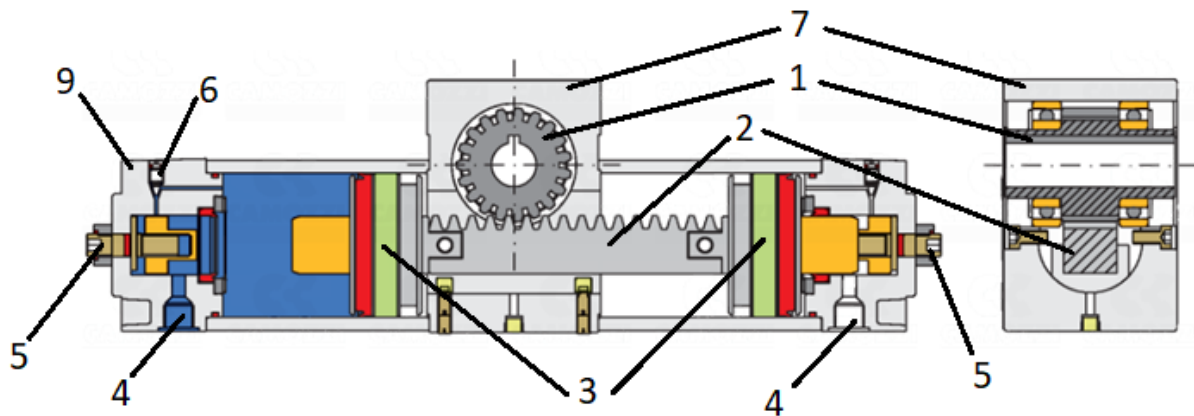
69 серія. Поворотний пневмоциліндр: 1 – втулка із шестернею; 2 – рейка із зубцями; 3 – поршень; 4 – підвідний канал для подачі надлишкового тиску; 5 – гвинти для регулювання; 6 – демпферні гвинти; 7 – корпус; 9 – бокові кришки.
